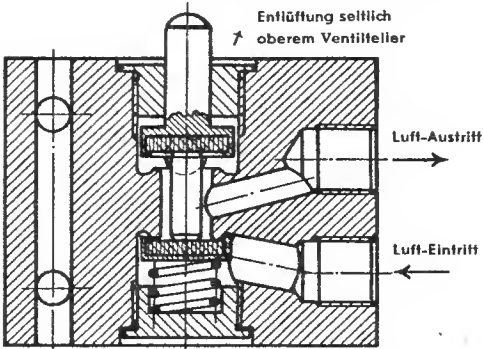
Steuer-Nockenventil, Grundtype 1 für Dreiwegesteuerung
